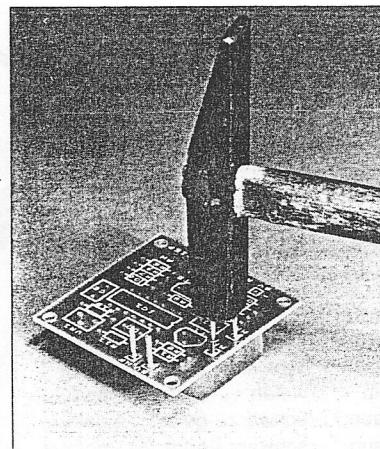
Das Hämmchen sorgt für den nötigen Druck beim Pin-Einpressen.
